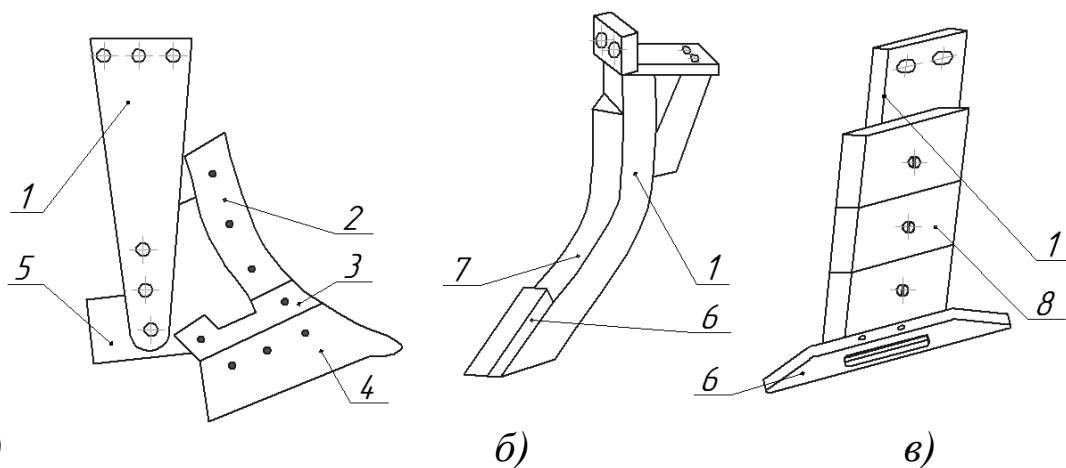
Формы рабочих поверхностей отечественных плужных корпусов
